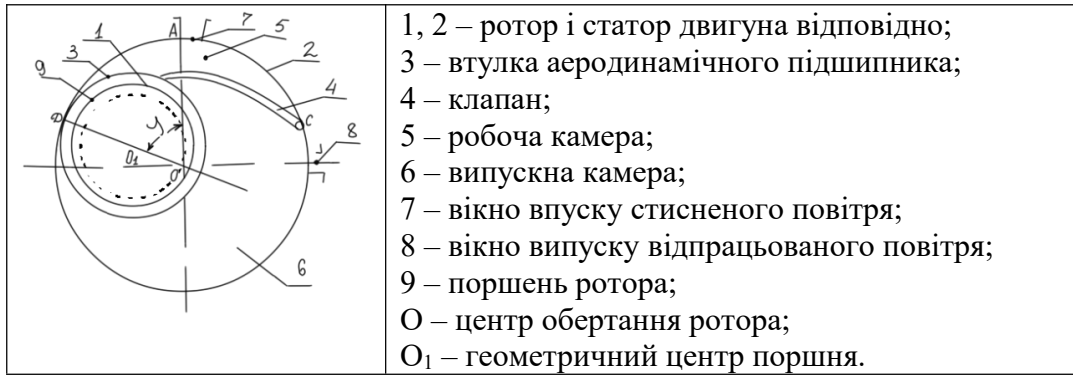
Принципова схема пневматичного ротаційно-поршневого двигуна
